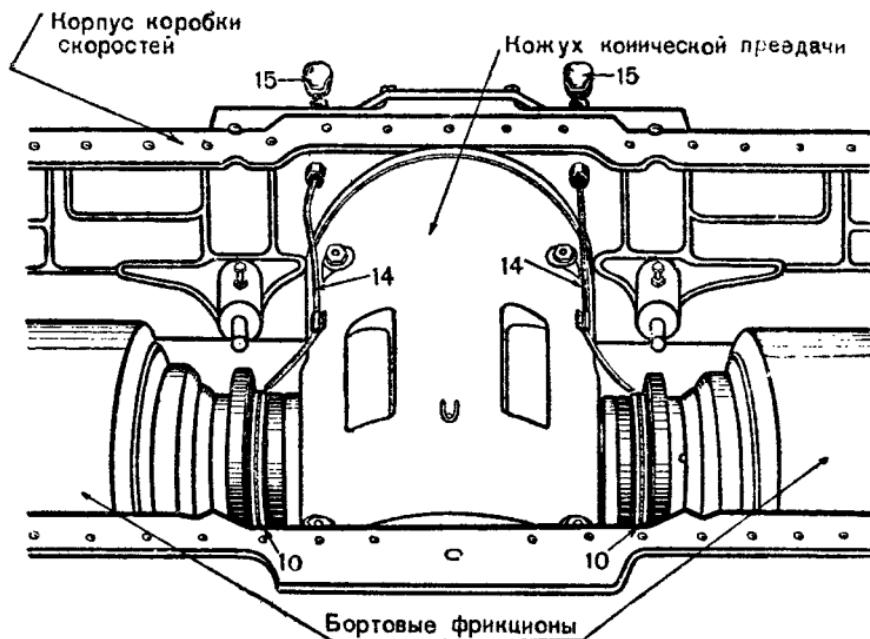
Смазка упорных шарикоподшипников бортовых фрикционов.
